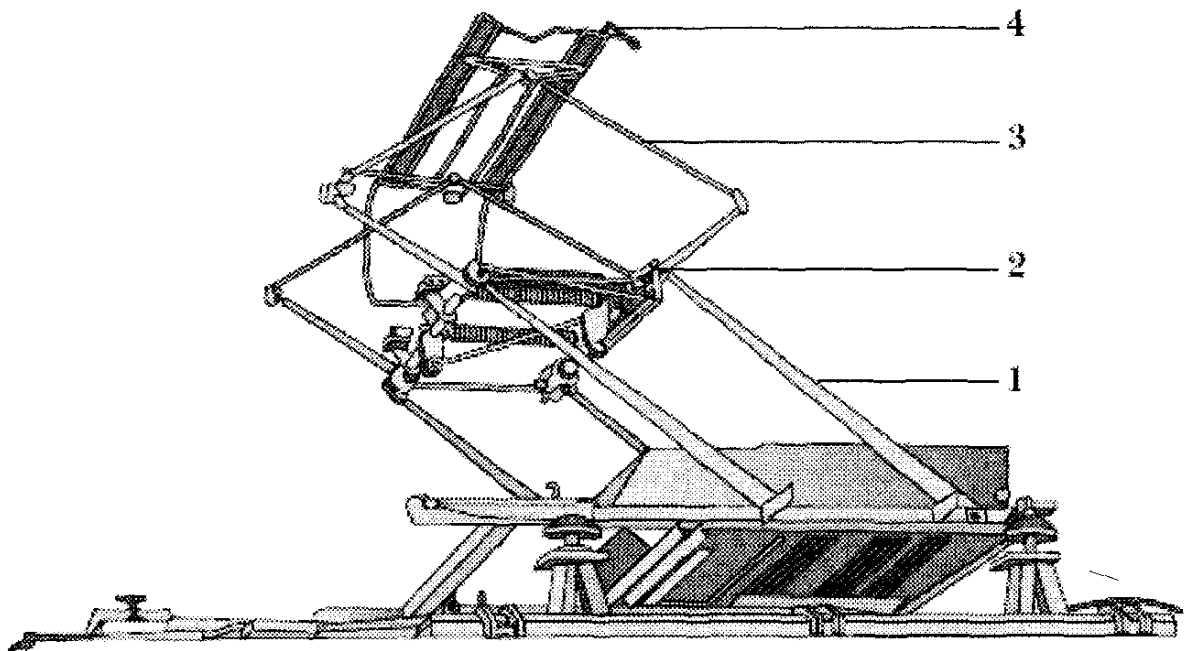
Двоярусний струмоз'ємний механізм для високошвидкісного електрорухомого складу залізниці: 1 — нижня рухома рама; 2- шарнірне з'єднання нижньої та верхньої рам; 3 - верхня рухома рама; 4 - полоз.
